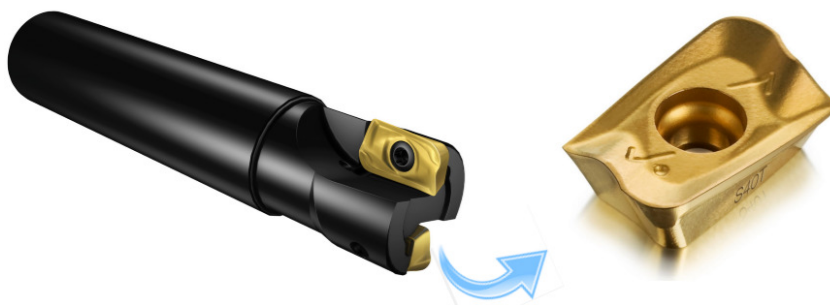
Fresa Sandvik Coromill® 390 adaptada utilizada para a remoção do material remanescente do pino consumível (SANDVIK, 2016).
